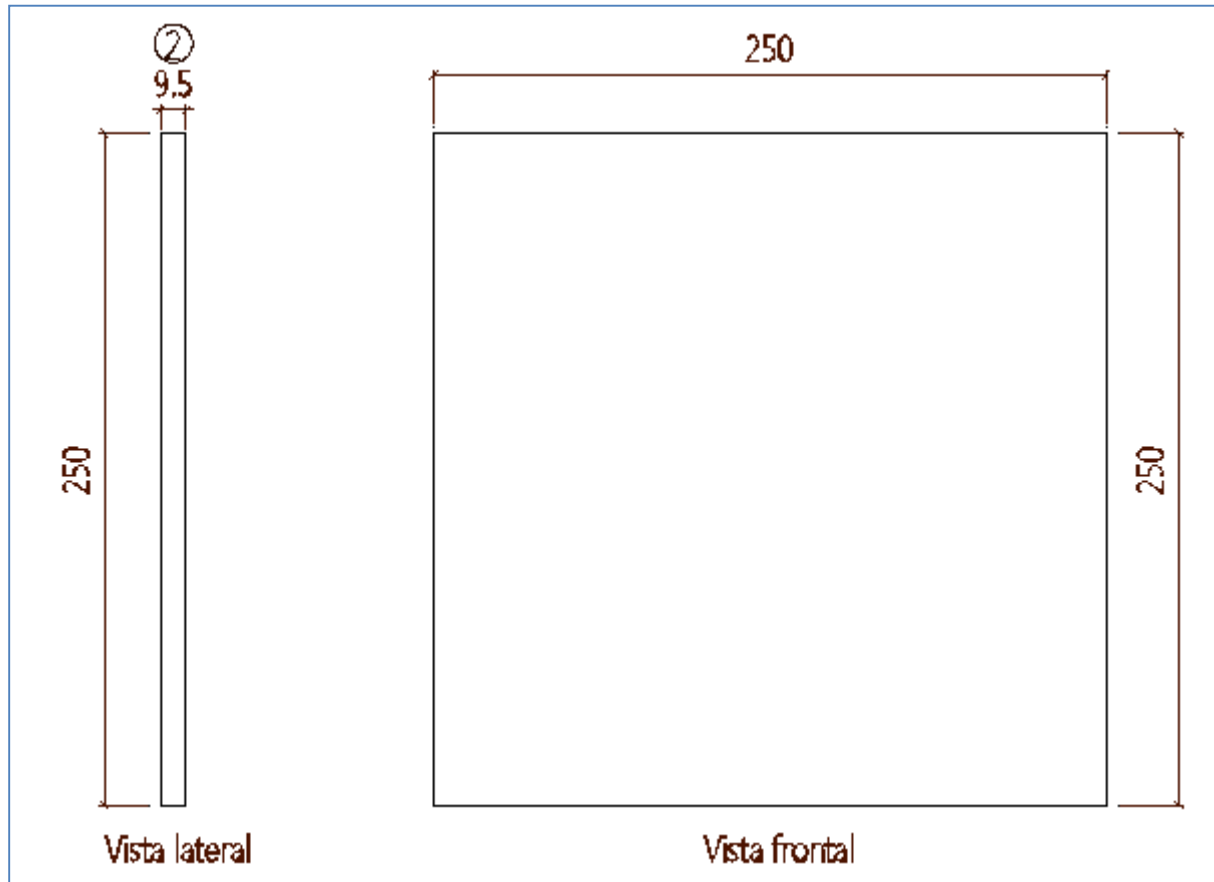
Detalle despiece pieza No.2 modelo 3 tensión.
